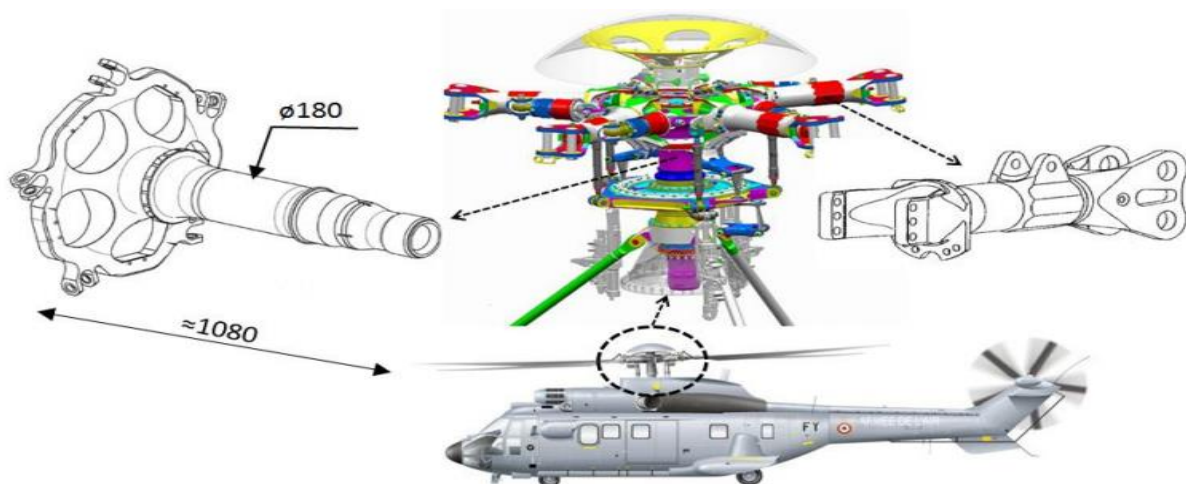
Positionnement du mât rotor et du manchon de fixation de pale : pièces critiques en 15-5PH usinées en tournage finition [17].
